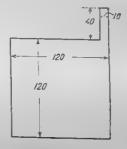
Размеры и форма пластин (из рольного свинца) для и готовления аккумулятора накала.
